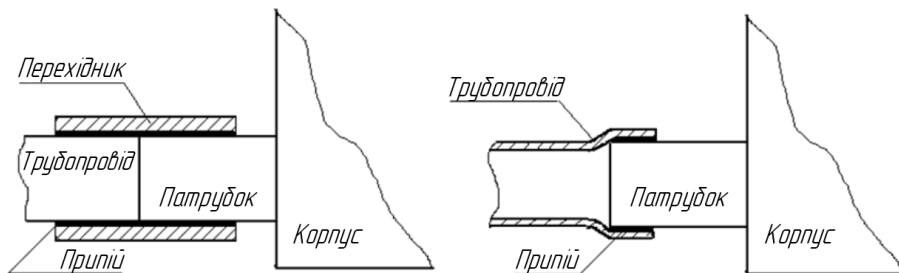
Способи з'єднання патрубка агрегату компресорного з трубопроводом
